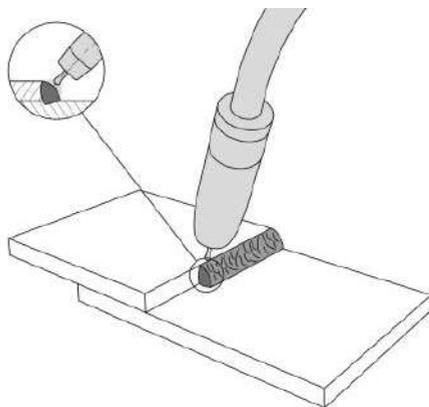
Вылет сварочной проволоки.
